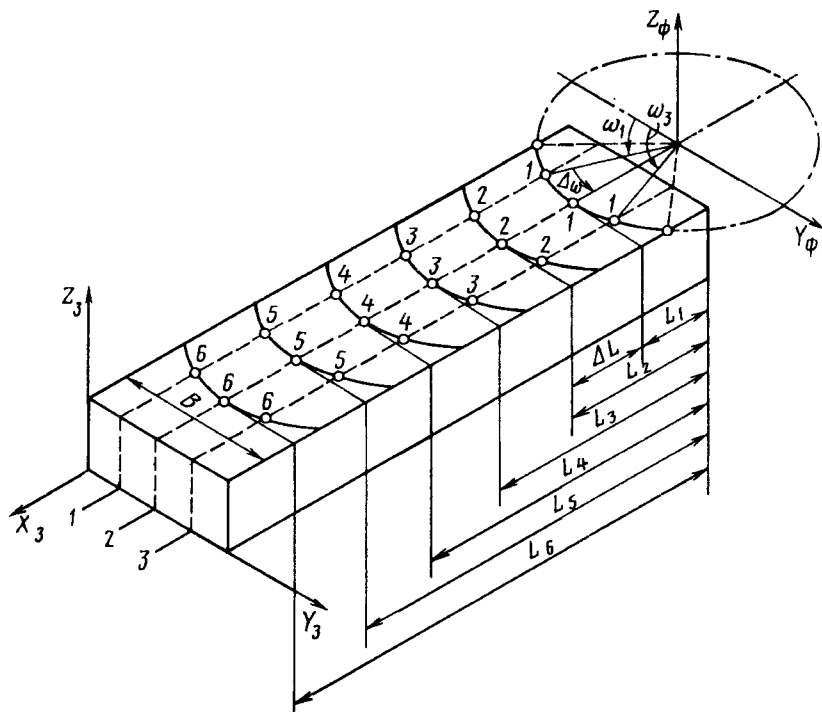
Заготовка, обрабатываемая на фрезерном станке
